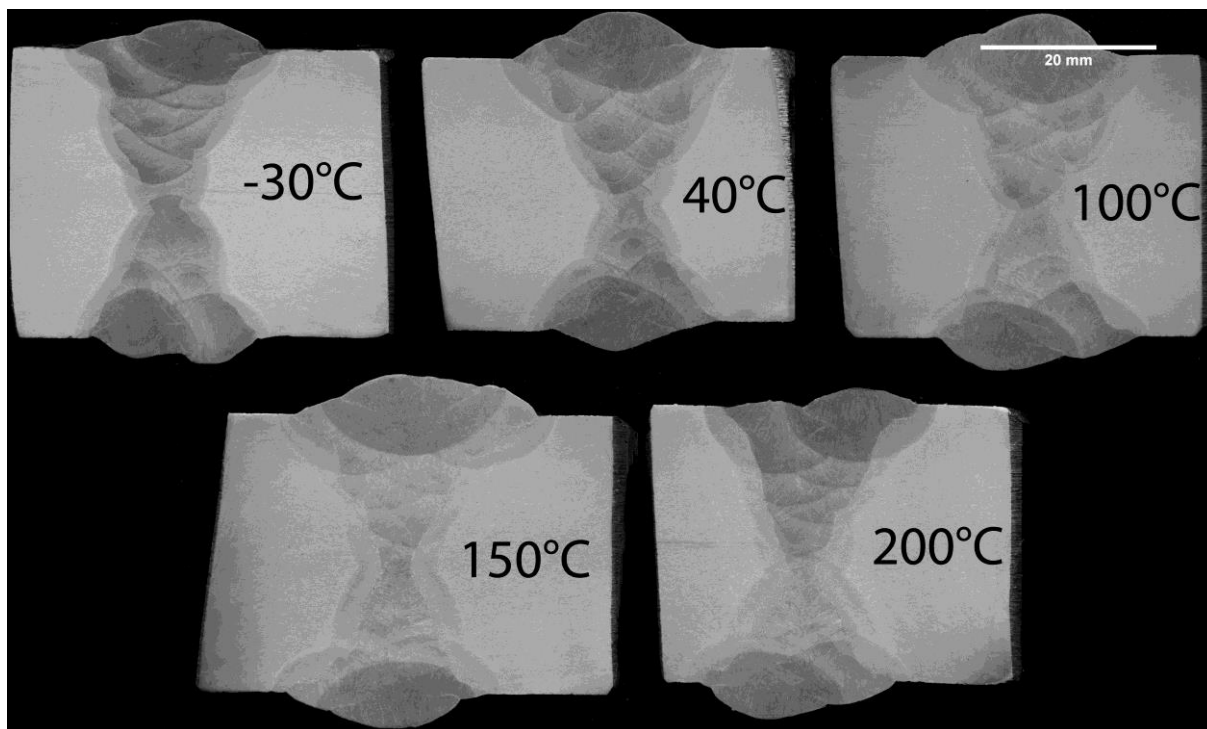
Macrofotografias das juntas soldadas.
